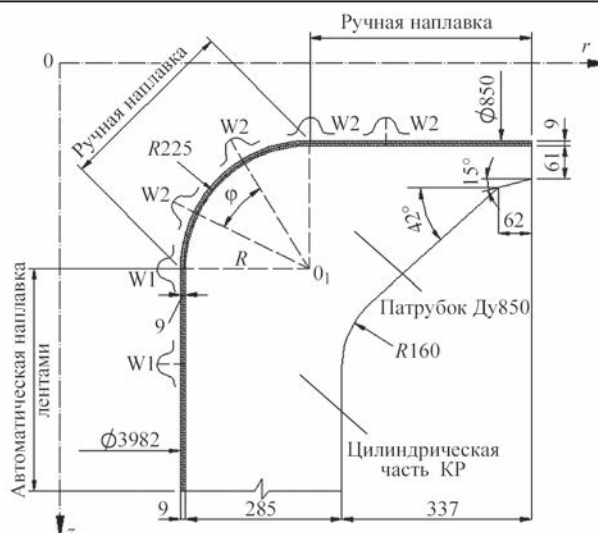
Схема патрубковой зоны КР и расположение участков с различными технологиями дуговой наплавки
